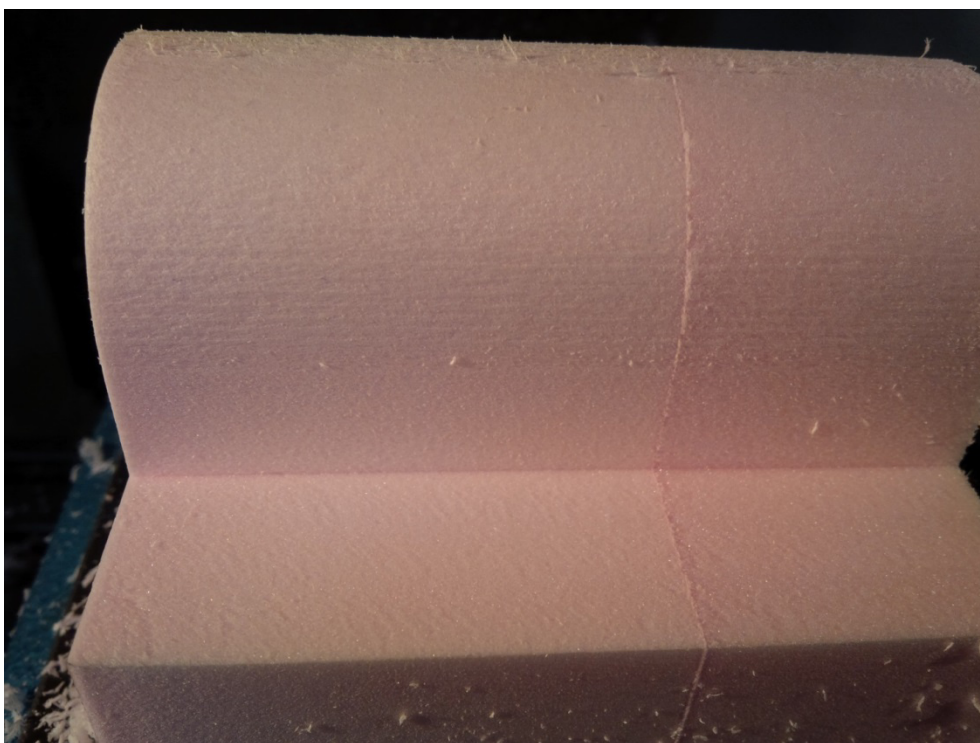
Obrábění EPS se od předchozích testů PUR pěn liší větší houževnatostí materiálu a nižší porézností, jehož třísky tak mají větší soudržnost a tvoří delší kusy a v některých případech i chuchvalce. Původně zvolenými nástroji šly testované vzorky obrábět dobře, ovšem po dokončovací operaci zůstávají na povrchu jemné chloupky. Nejpatrnější je tento jev na P2, to může být způsobeno pouze více kontrastní barvou materiálu.
